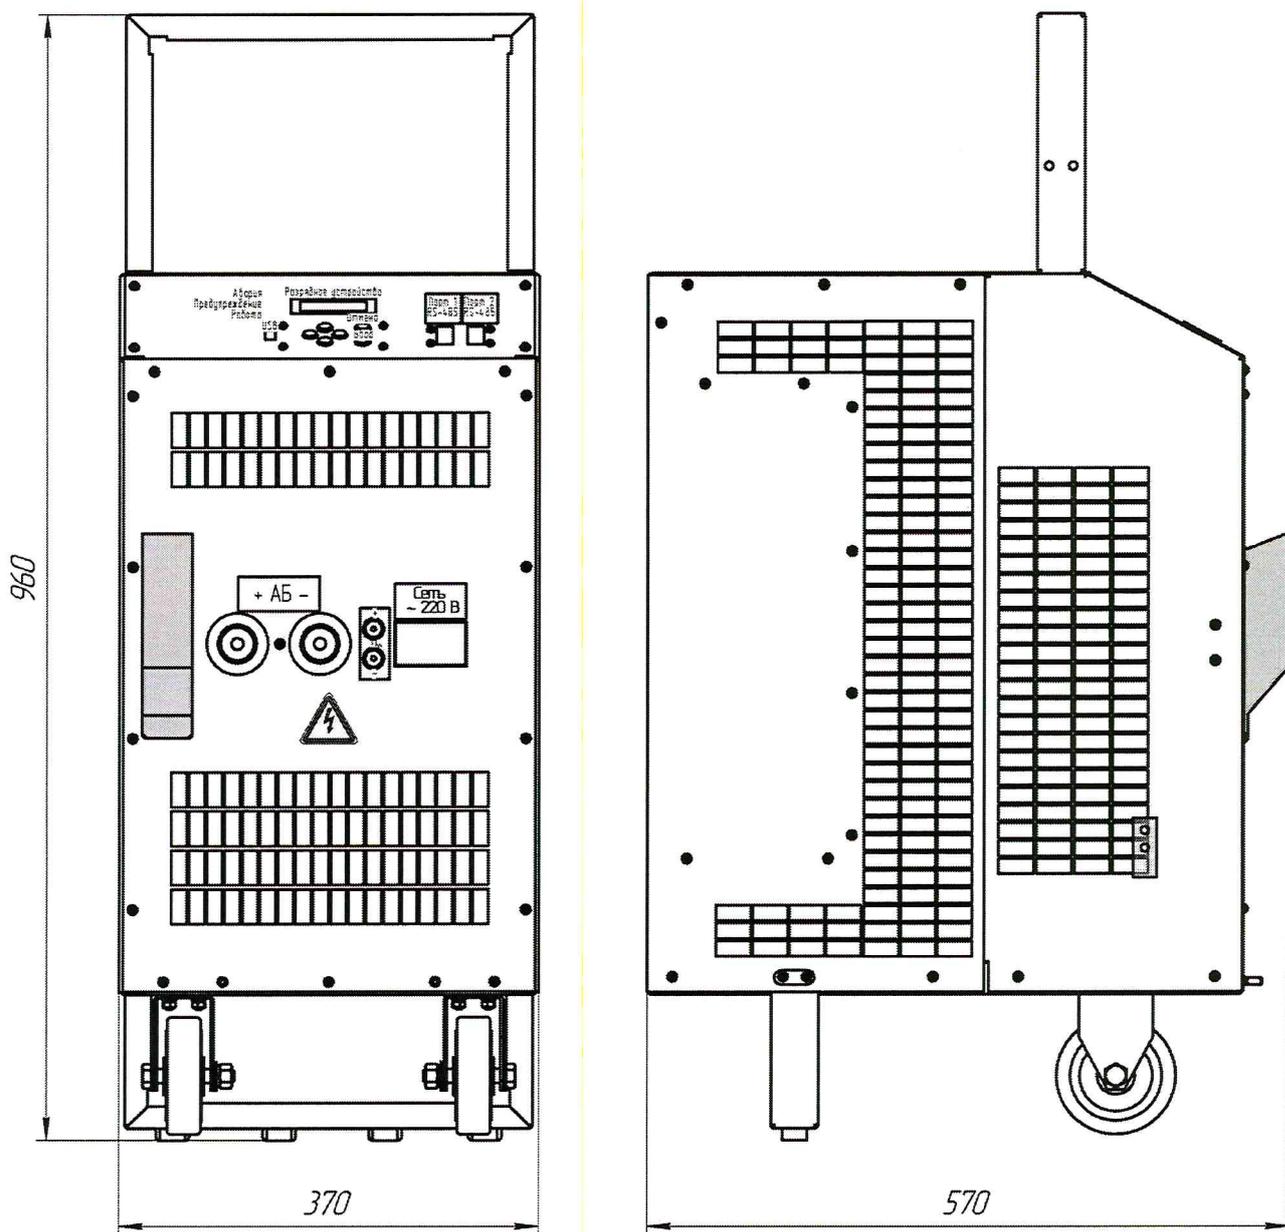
Общий вид и габаритные размеры СКР-50
